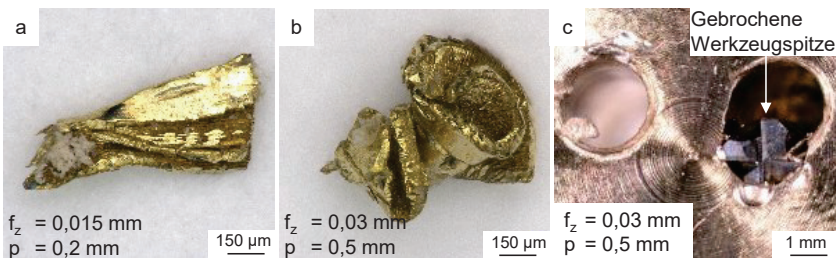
Beispiele für deformierte Späne beim Tauchfräsen von CuZn42 mit Werkzeug C (a, b) und dadurch verursachter Werkzeugbruch (c)
